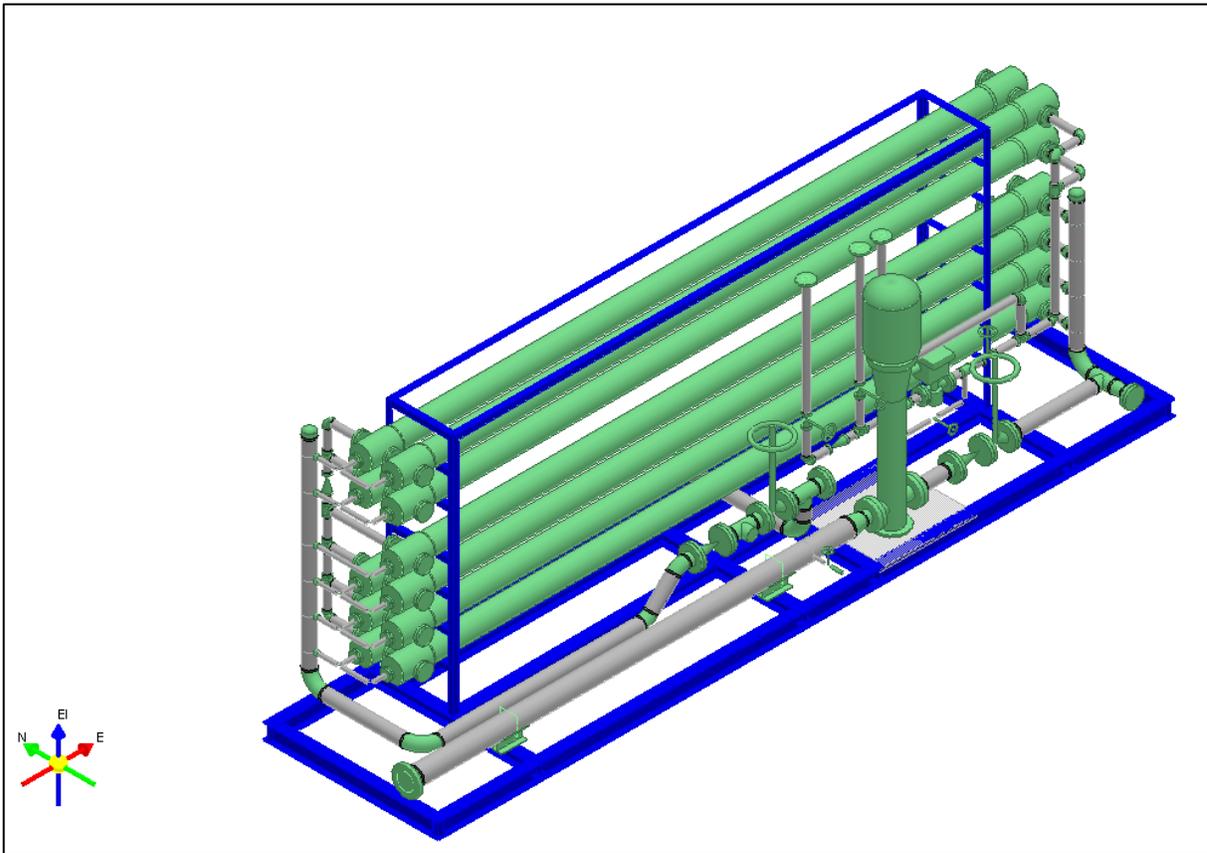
Maqueta electrónica del diseño de Ósmosis inversa (vista isométrica).
